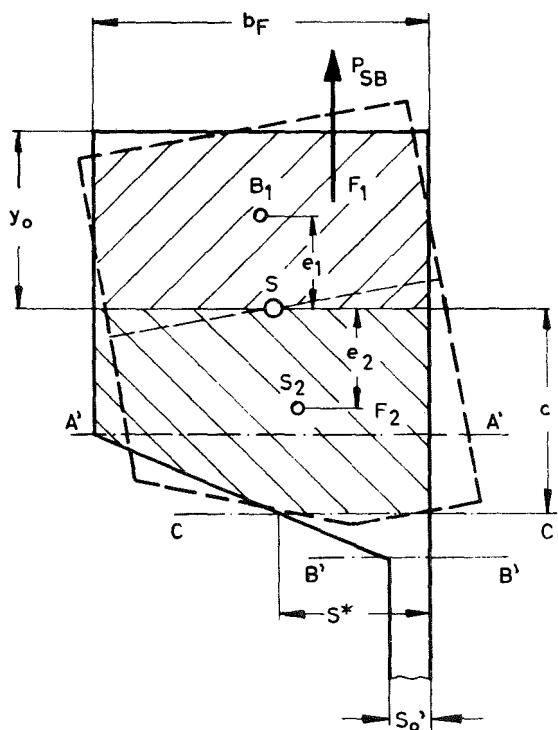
Drehung des Flanschrings um den Schwerpunkt
